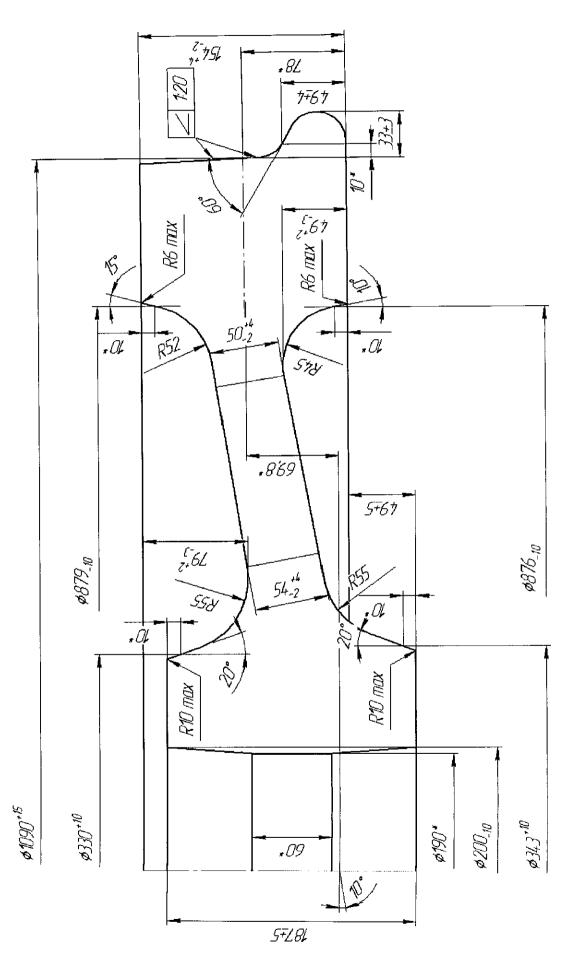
Черновое колесо Ø 1090 мм (под чистовое Ø 1076 черт. № КР-0008-10). Масса колеса – 817 кг.
